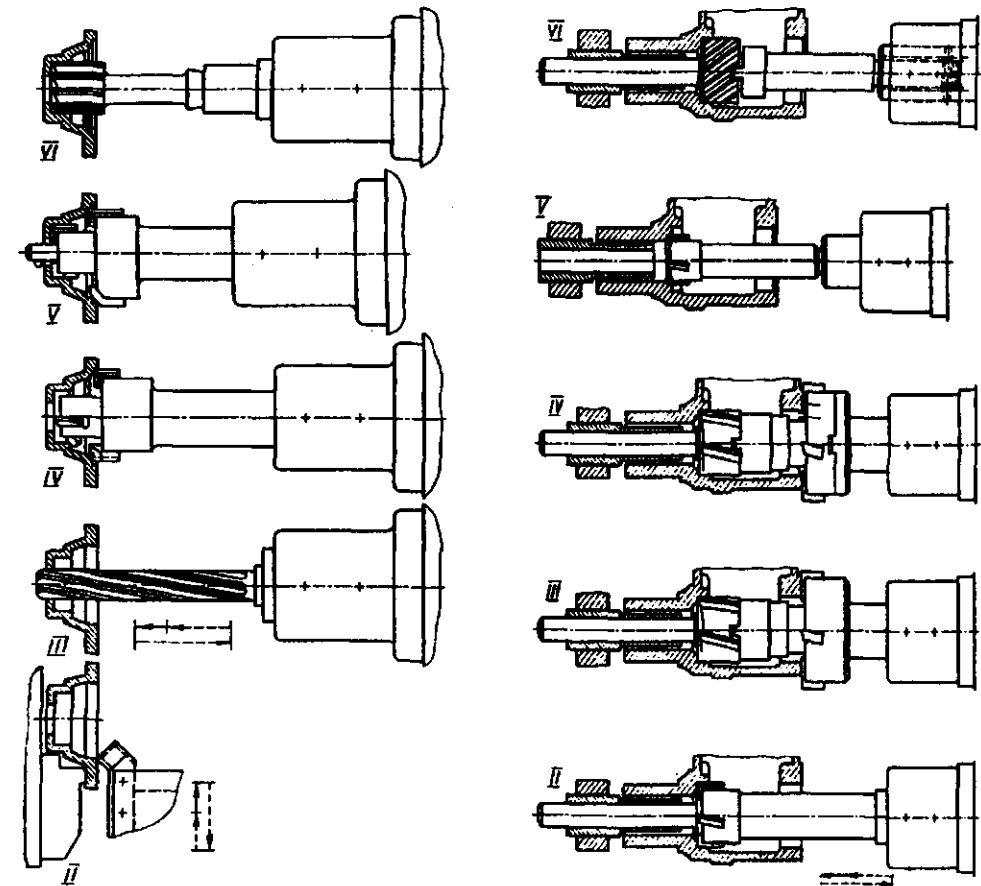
Схемы обработки крышки из штучной заготовки: I – снять и закрепить заготовку (не показано); II – подрезать торец; III – зенкеровать центральное отверстие диаметром 24 мм; IV – предварительно расточить отверстия диаметром 44,5; 71 и 80 мм; снять фаску; V – окончательно расточить отверстия диаметром $25^{+0,21}$ и $72^{+0,12}$ мм; предварительно расточить отверстие диаметром 45,5 мм и притупить острые кромки; VI – развернуть отверстие диаметром $46^{+0,062}$ мм
